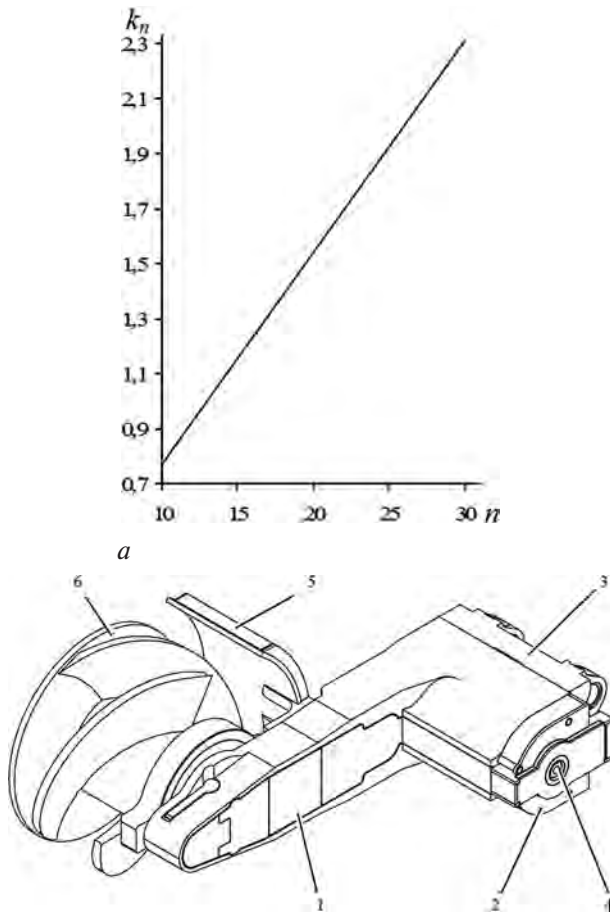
График зависимости k_n от n (a) и схема узла резания (b): 1 — поворотный редуктор; 2 — двигатель привода режущего органа; 3 — держатель поворотного редуктора; 4 — муфта включения со срезным валом; 5 — погрузочный щиток; 6 — режущий шнек с резцами
